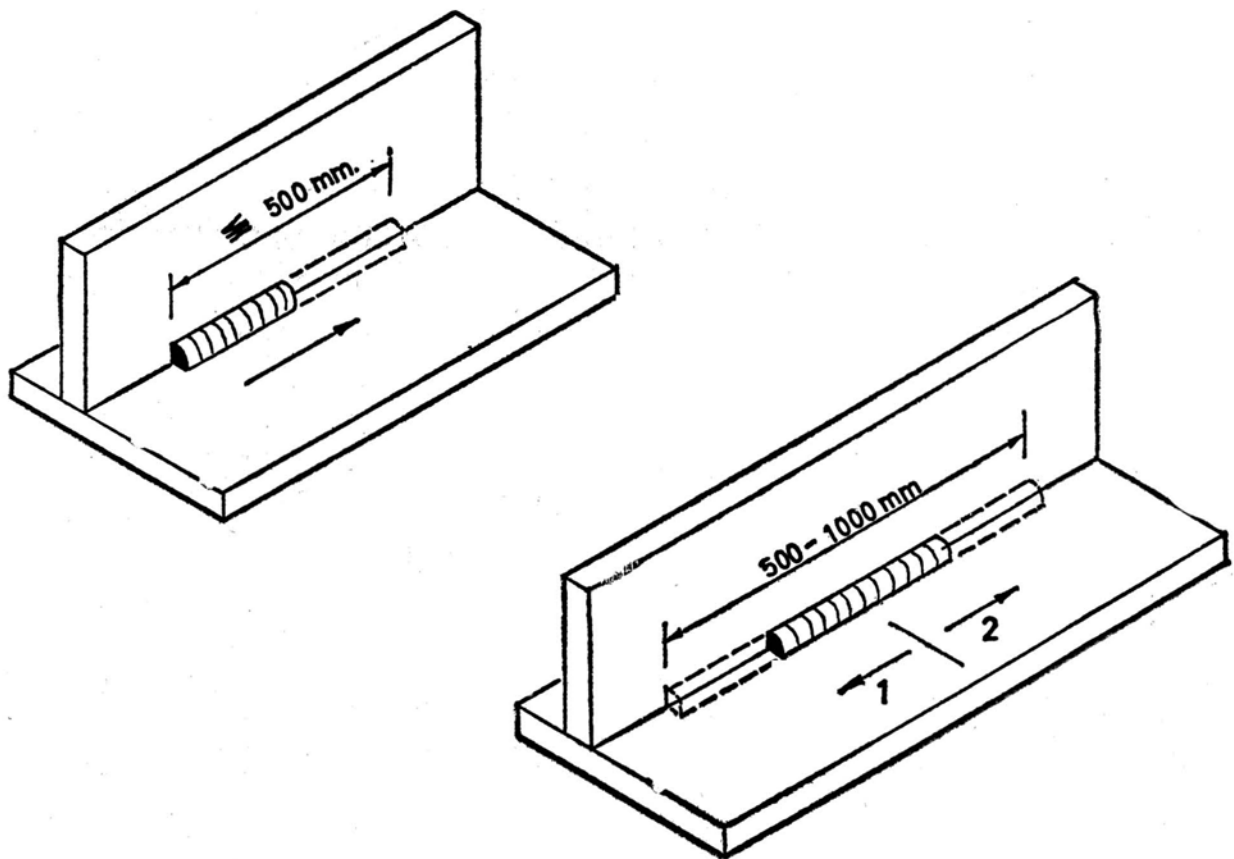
EJECUCION DE SOLDADURAS
